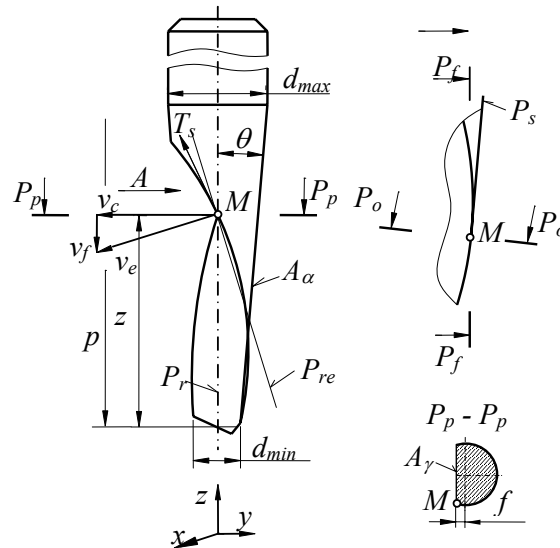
Общий вид конической развертки и положение инструментальных координатных плоскостей
